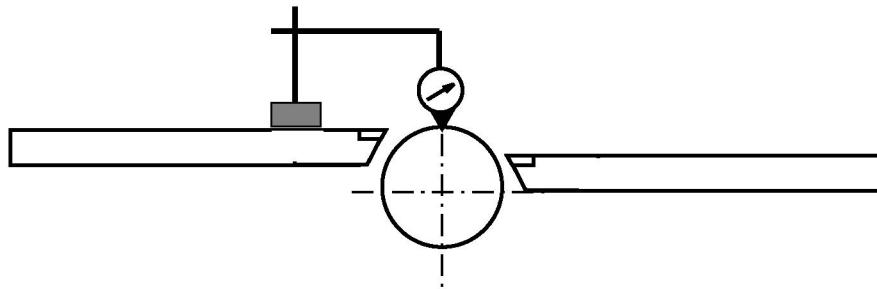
Схема проверки параллельности ножевого вала к заднему столу
